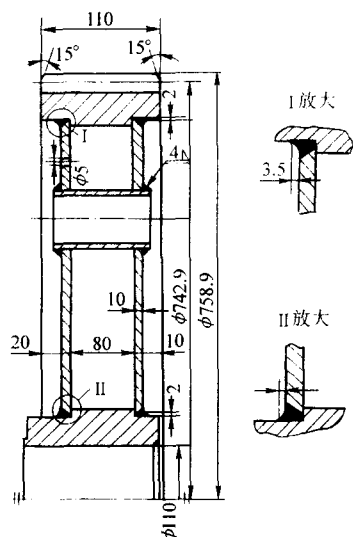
双辐板式焊接圆柱斜齿轮
